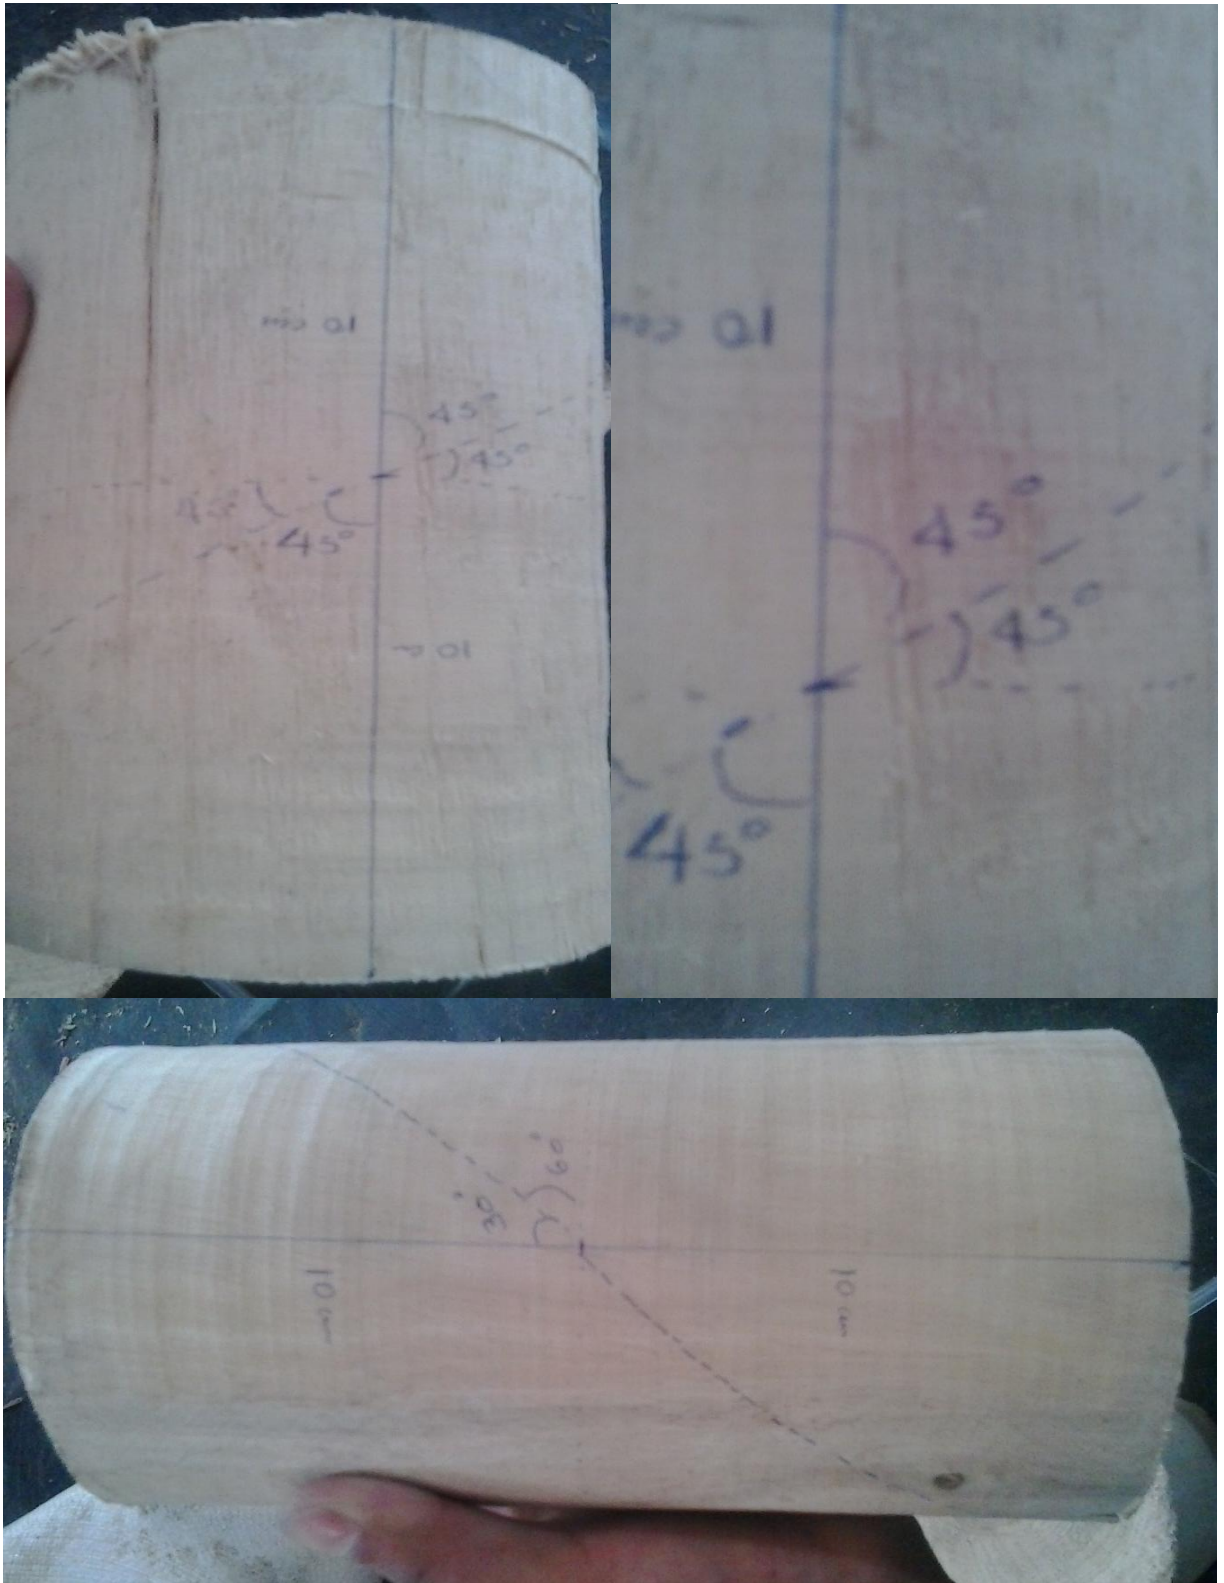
Madera utilizada en forma de cuña para los ángulos de 30° y 45°
